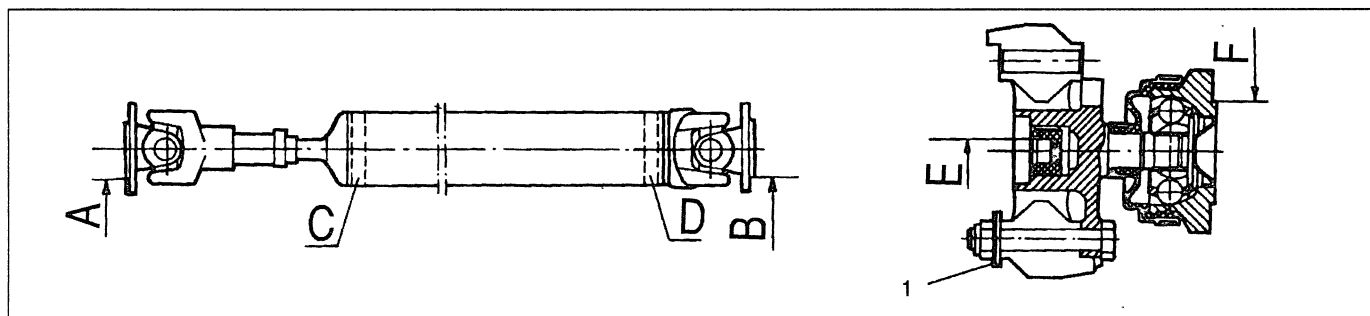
Балансировка карданных валов: 1 – шайбы для балансировки; А, В, Е, F – поверхности контроля дисбаланса; С, D – опорные поверхности вала на балансировочной машине
